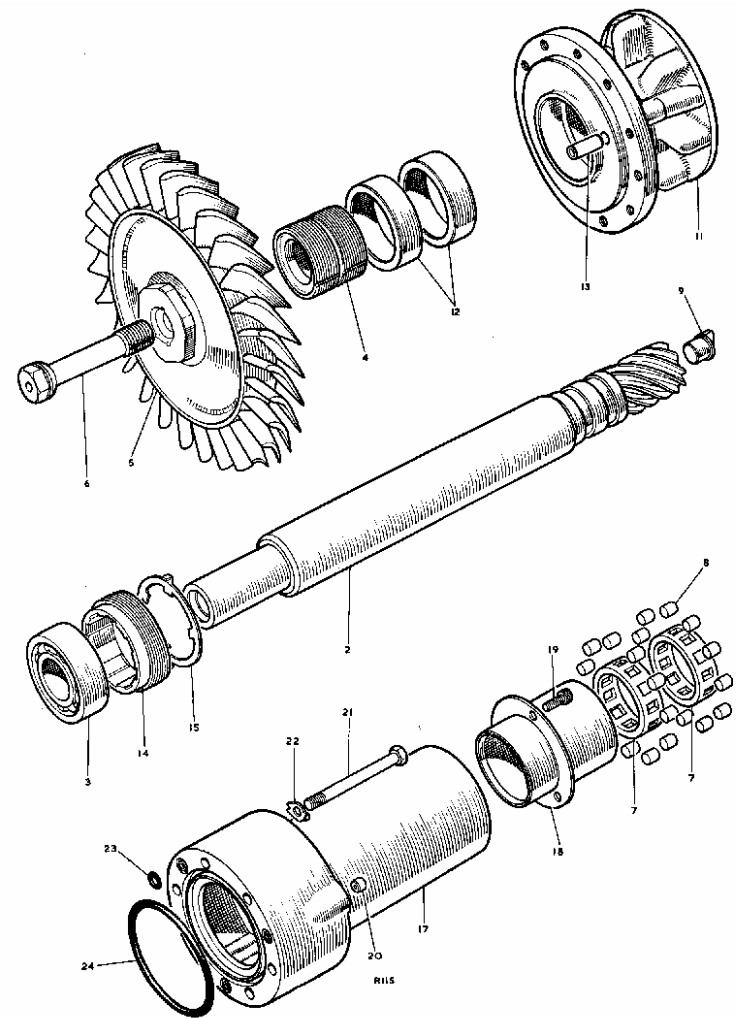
Explosionszeichnung der Nutzleistungsturbine [5]
